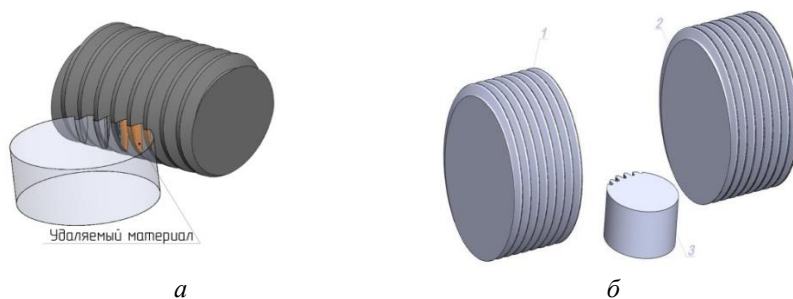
Виртуальная модель обработки зубчатого колеса:
